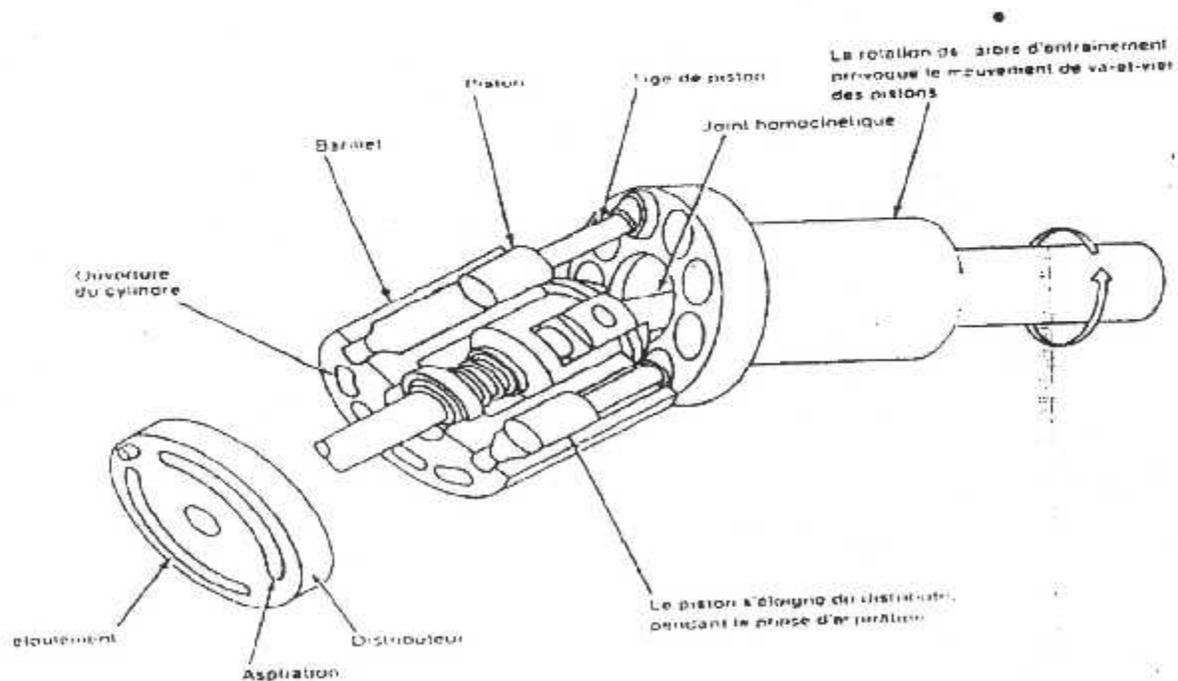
Coupe de la pompe a barillet (Dessin : vickers)
